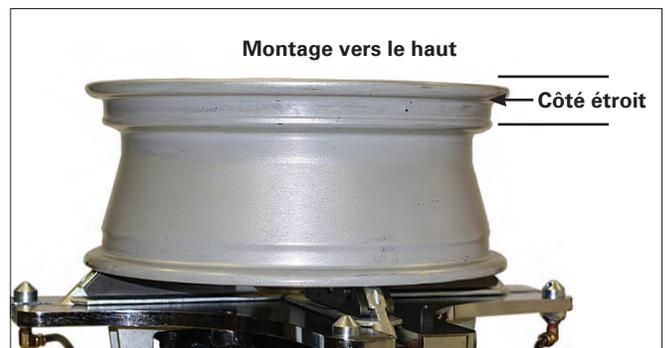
Placer l'ensemble de pneu/roue sur l'établi
